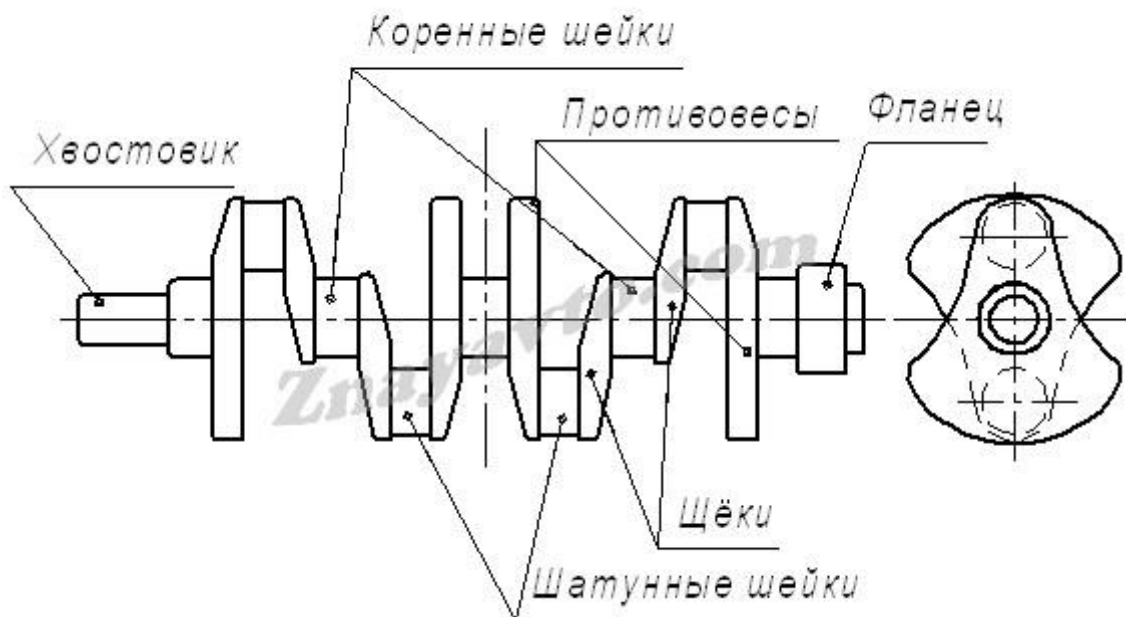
Коленчатый вал рядного четырехцилиндрового двигателя
